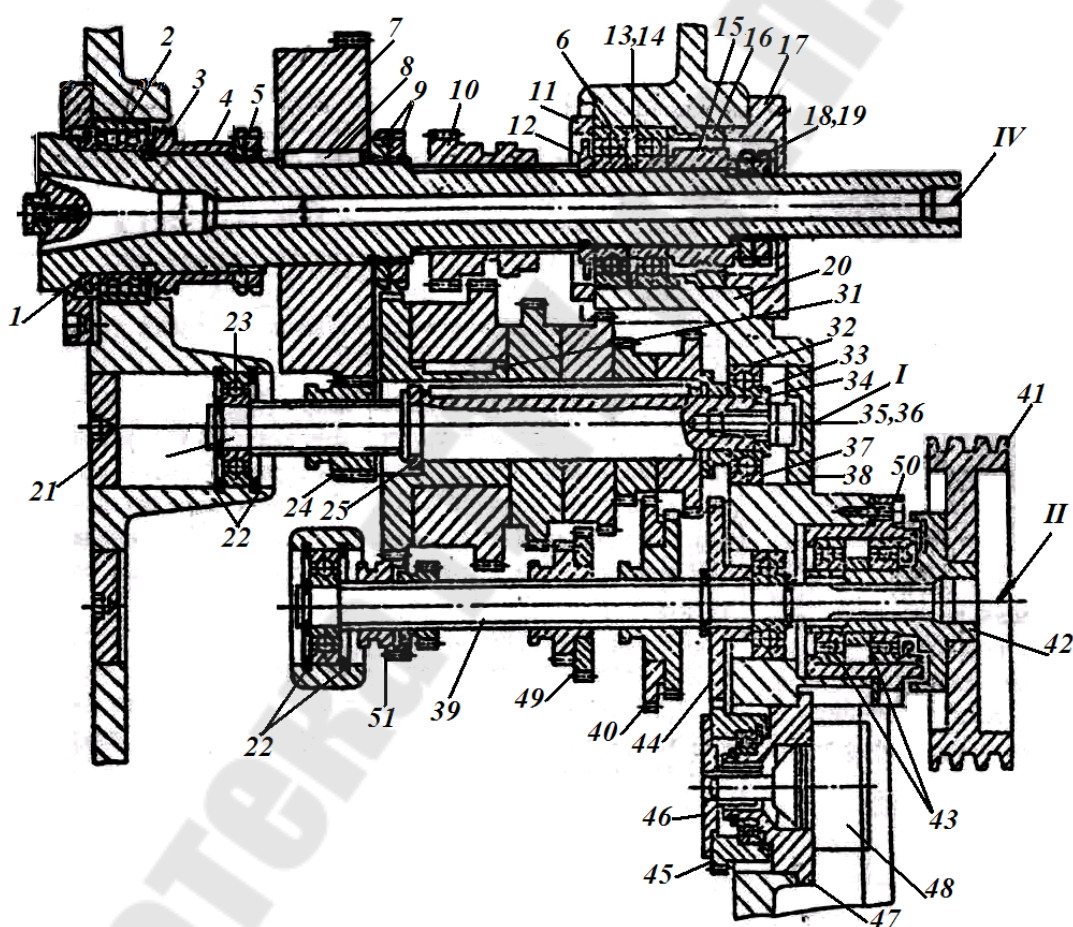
Коробка скоростей горизонтально-фрезерного станка
